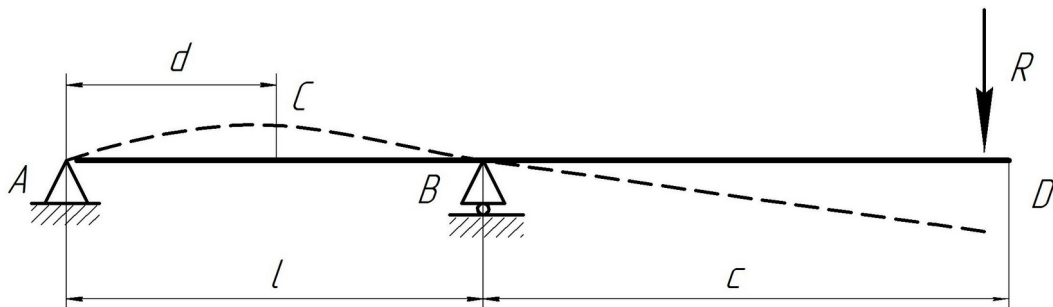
Розрахункова схема двохопорного веденого вала ГРА
